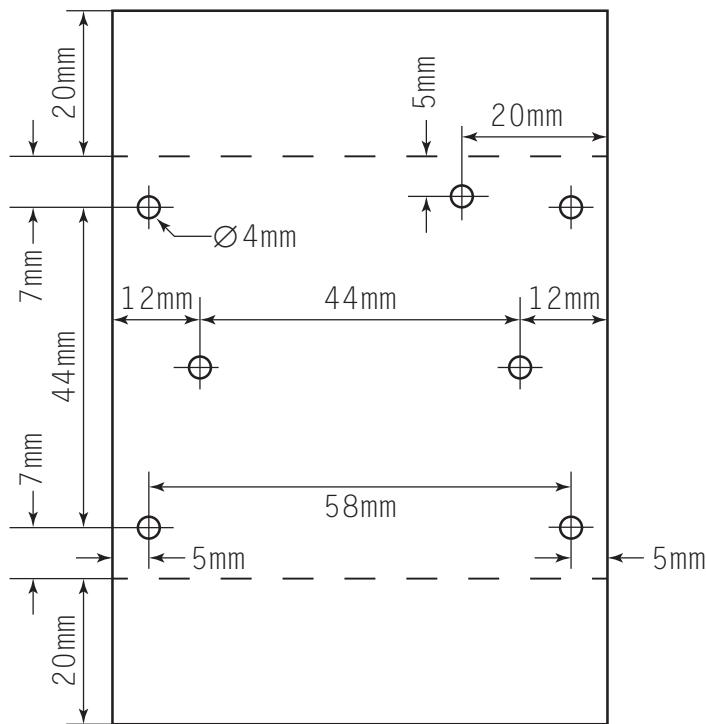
DISEÑO DEL CORTE DEL CHASIS DEL MÓDULO EXTERIOR
